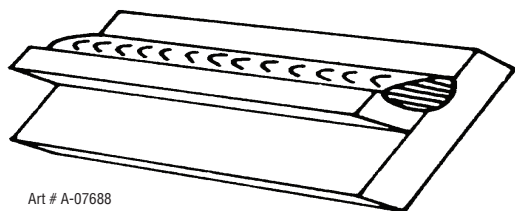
Soudure à plat, d'angle par gravité
